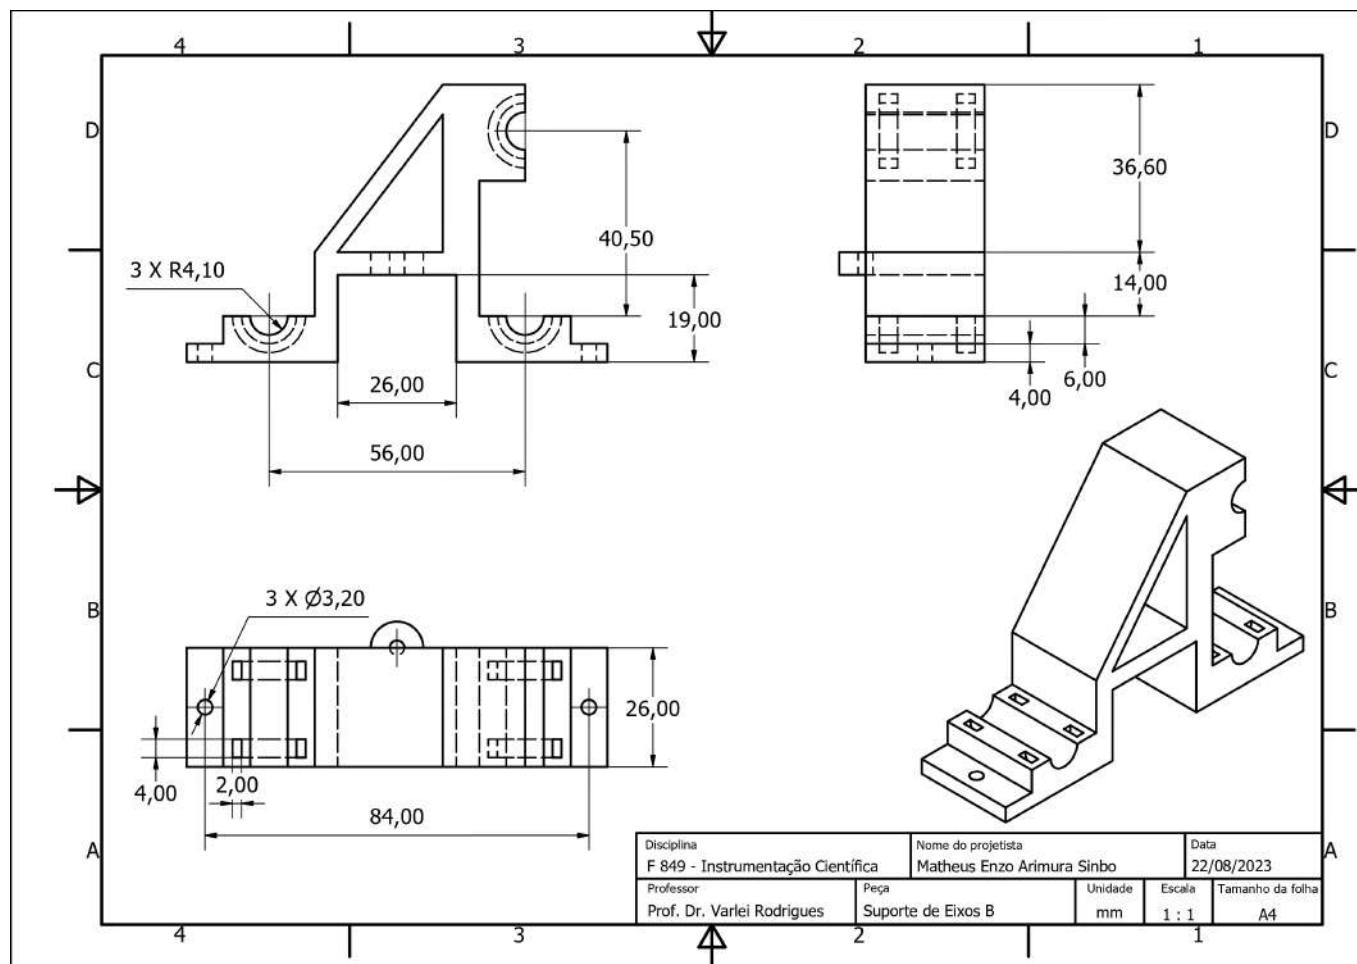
Desenho técnico do suporte dos eixos da carruagem para o lado B.
